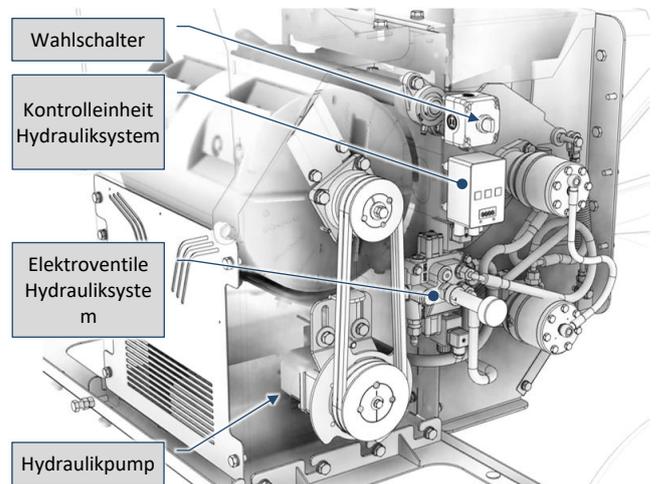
Detailansicht des Hydrauliksystems für die Zuführwalzen (rechte Seitenansicht ohne Schutz)
